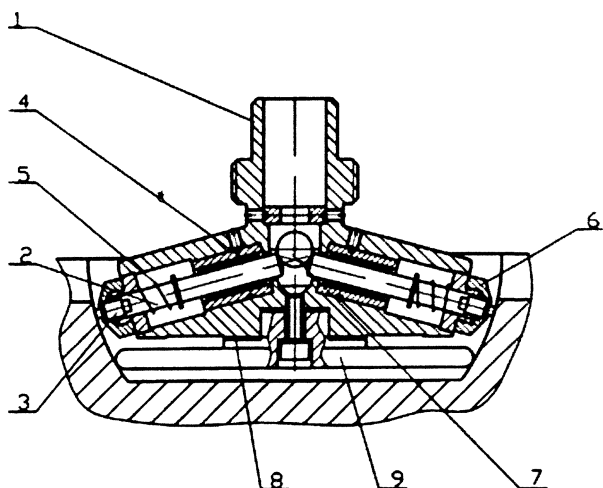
Конструкция инструментальной головки специального средства измерения для контроля номинально сферических элементов деталей:
